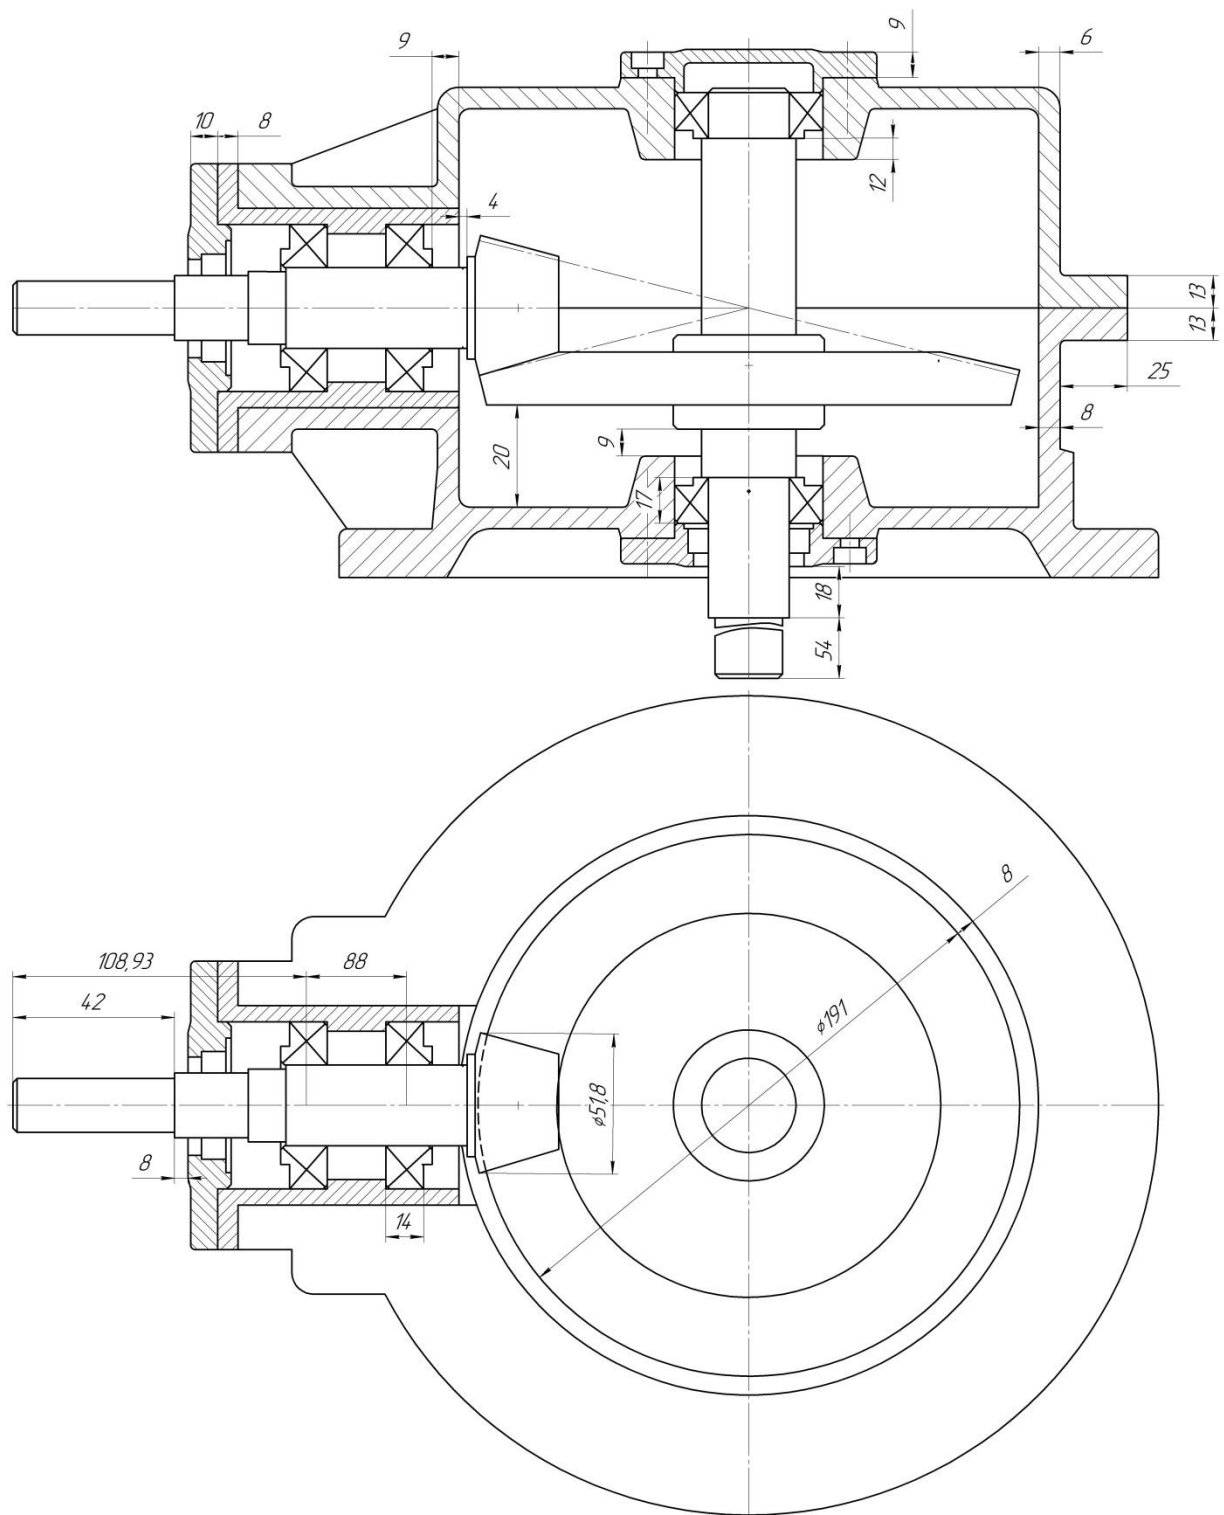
Ескізна компоновка конічного редуктора
